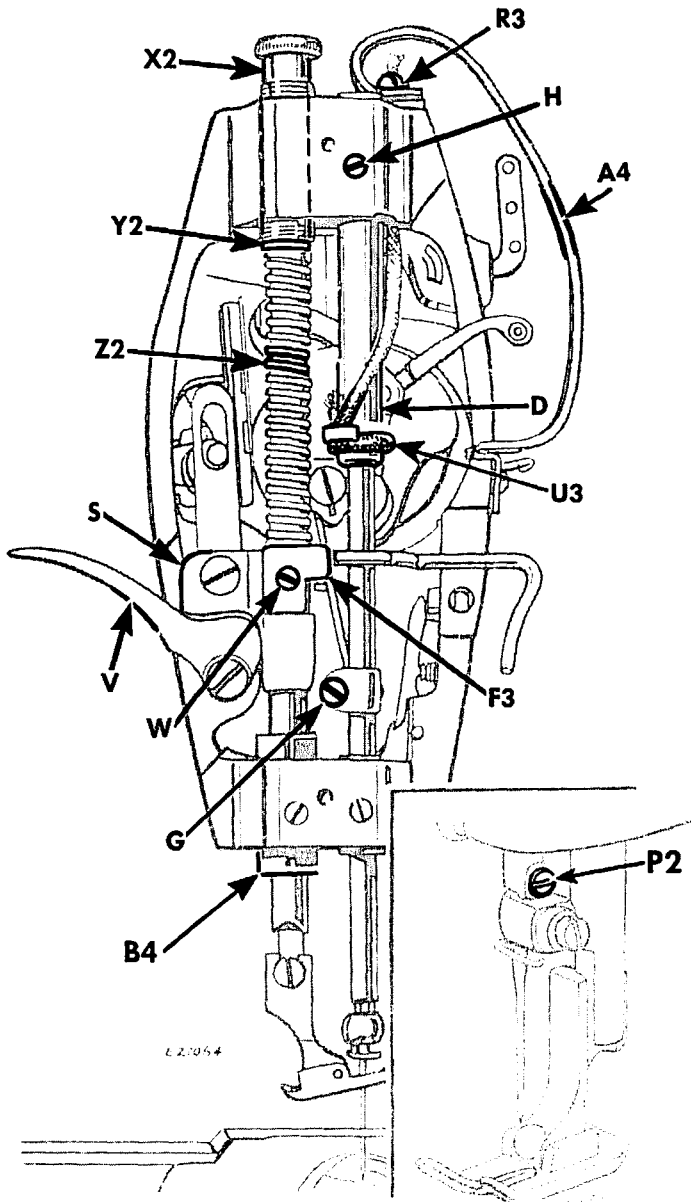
Assemblages de barre à aiguille et de barre du presseur
